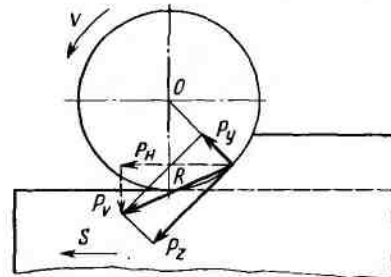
Силы сопротивления резанию при цилиндрическом фрезеровании
